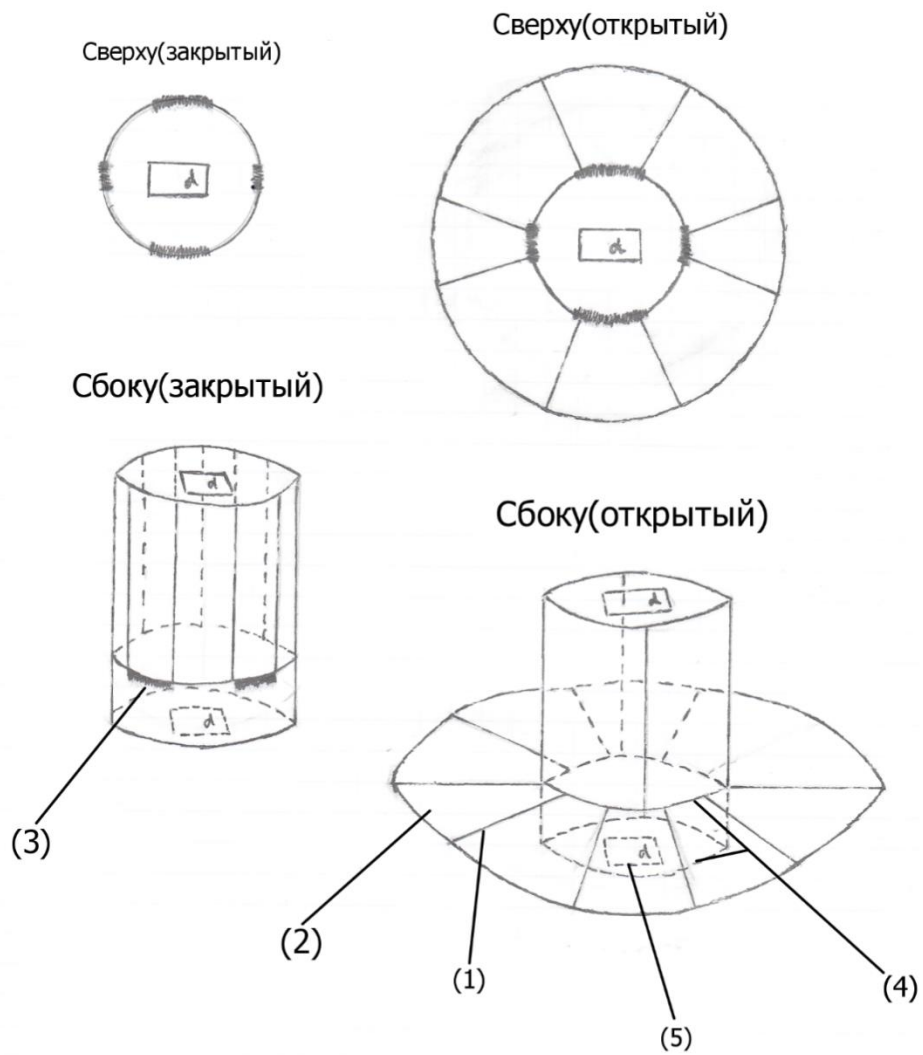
Чертёж авторской конструкции модуля с солнечным парусом (Первая версия): *металлический каркас(1), солнечный парус(2), гидравлические двигатели для обеспечения развёртывания солнечного паруса(3), аккумуляторный отсек(4), стыковочный отсек(5).
